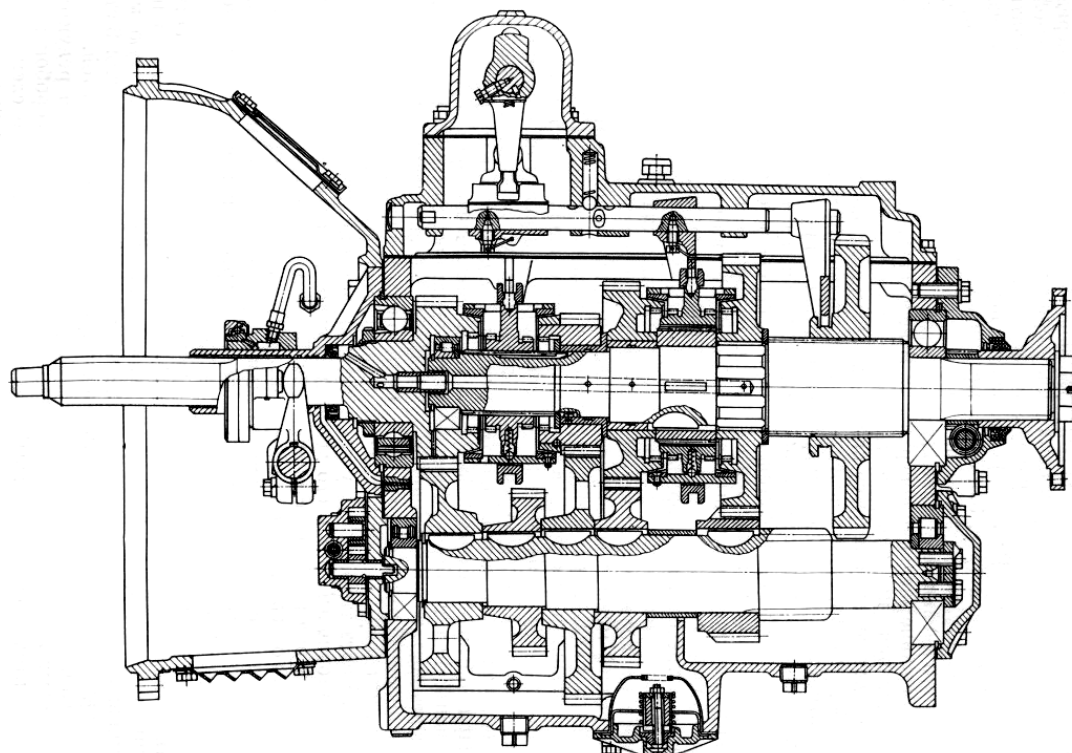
Конструкция коробки передач автомобиля МАЗ-500А
